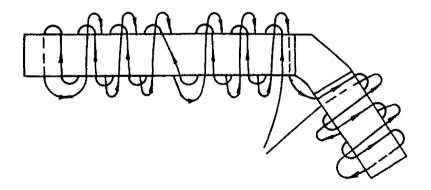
Схема намотки ДШ на корпус натяжного зажима.
